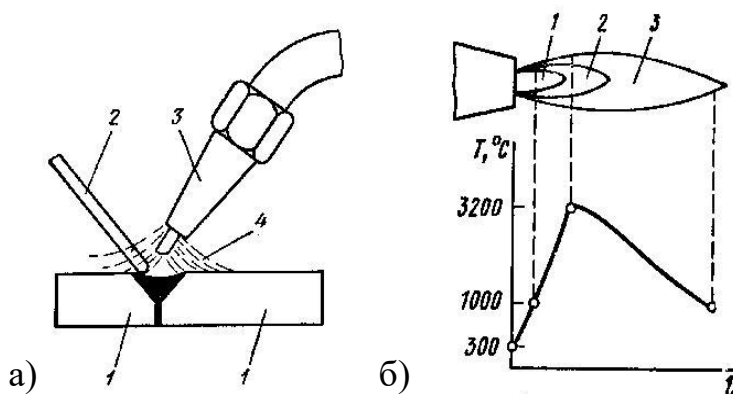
Газовая сварка: а) схема процесса: 1 – заготовка, 2 – присадочный материал, 3 – горелка, 4 – сварочное пламя; б) газосварочное пламя: 1 – ядро, 2 – сварочная зона, 3 – факел
